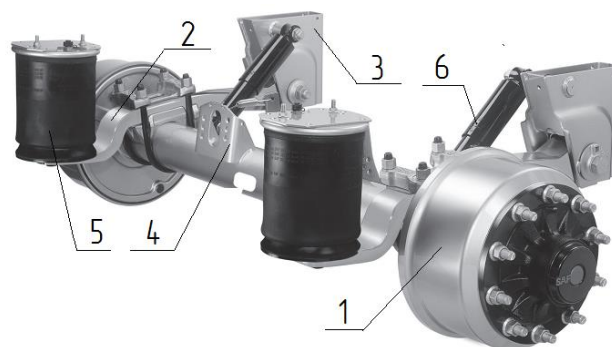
Осевой агрегат с пневматической подвеской на полурессорах.
